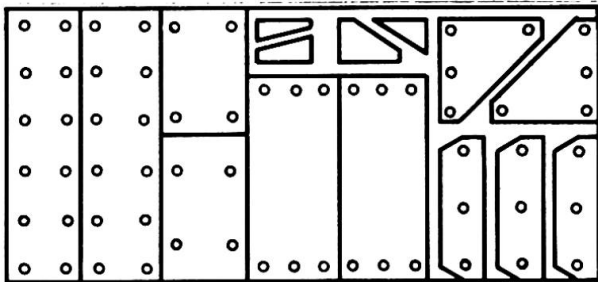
Exemple d'imbrication optimale de pièce à découper réalisée par machine à commande assistée par ordinateur.
